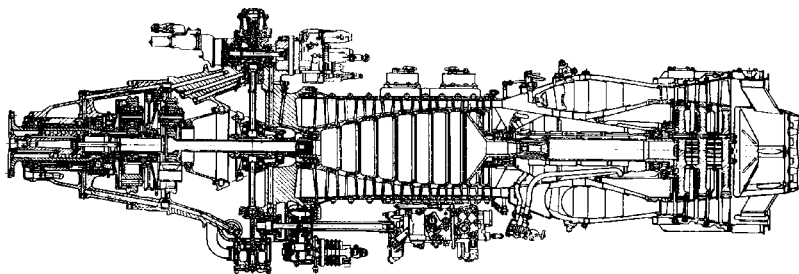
Газотурбинный двигатель типа АИ-20
